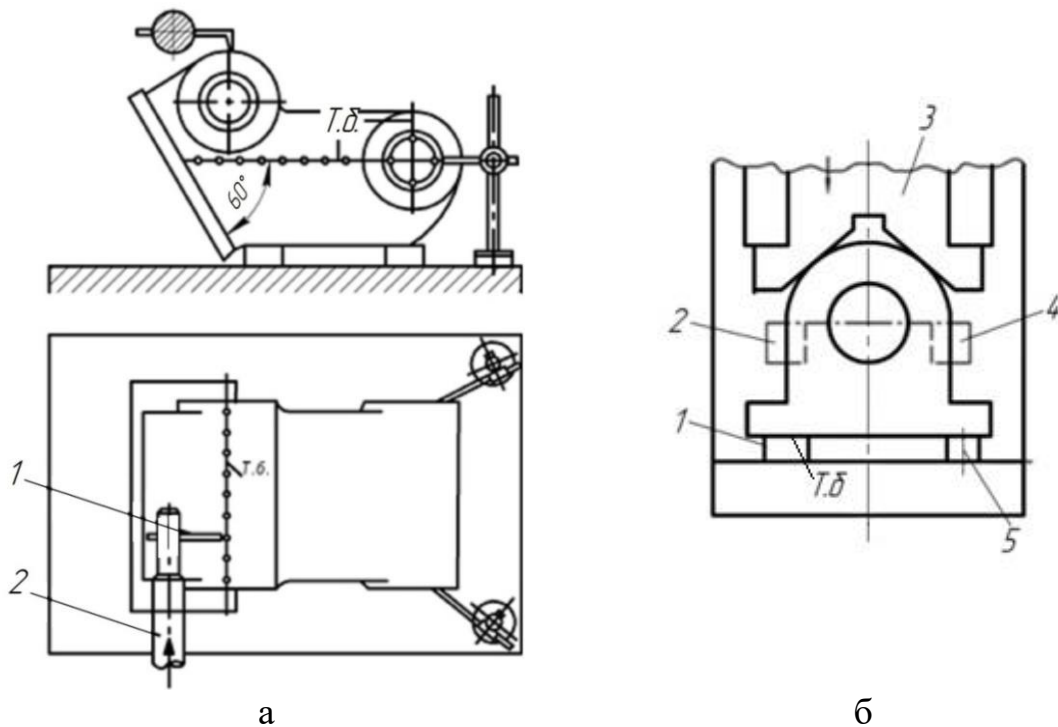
Реальное базирование заготовки выверкой по разметке (а) и сопряжением (б, 1 и 5 – опорные планки; 2 и 4 – упоры; 3 – подвижная призма)
